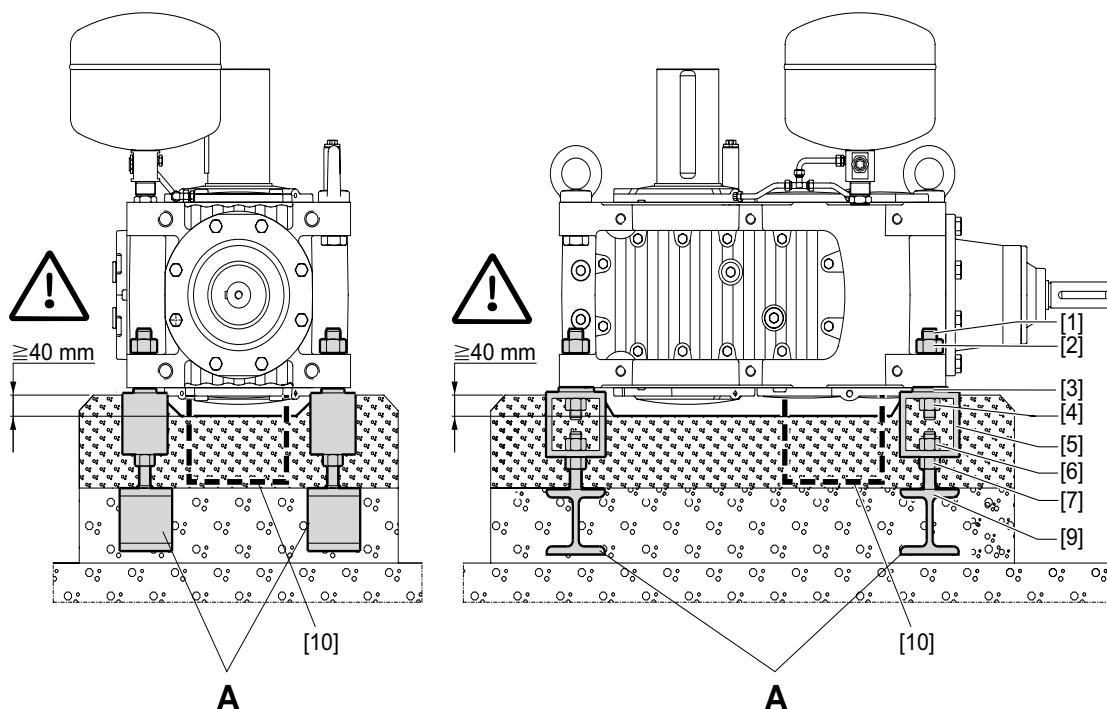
Fundament stalowo-betonowy dla przekładni przemysłowej MC.PE.. / MC.RE..
